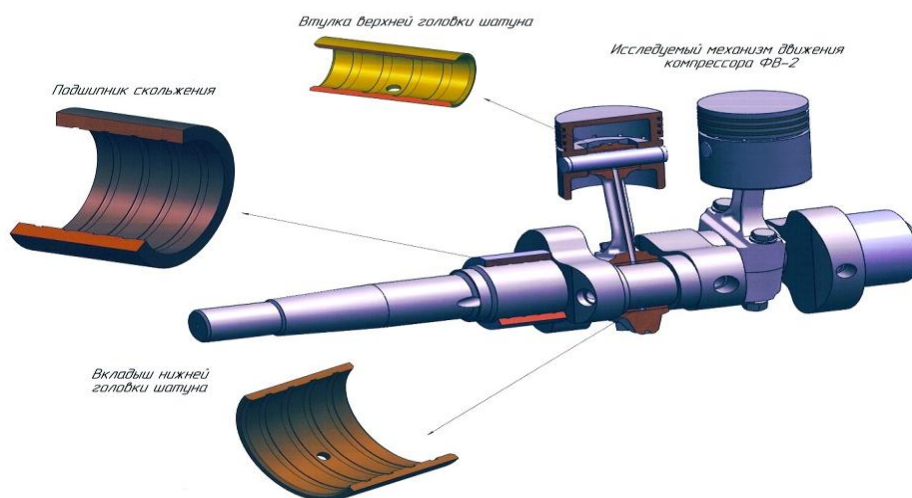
Конструкция вала с вкладышами с профилированными поверхностями
